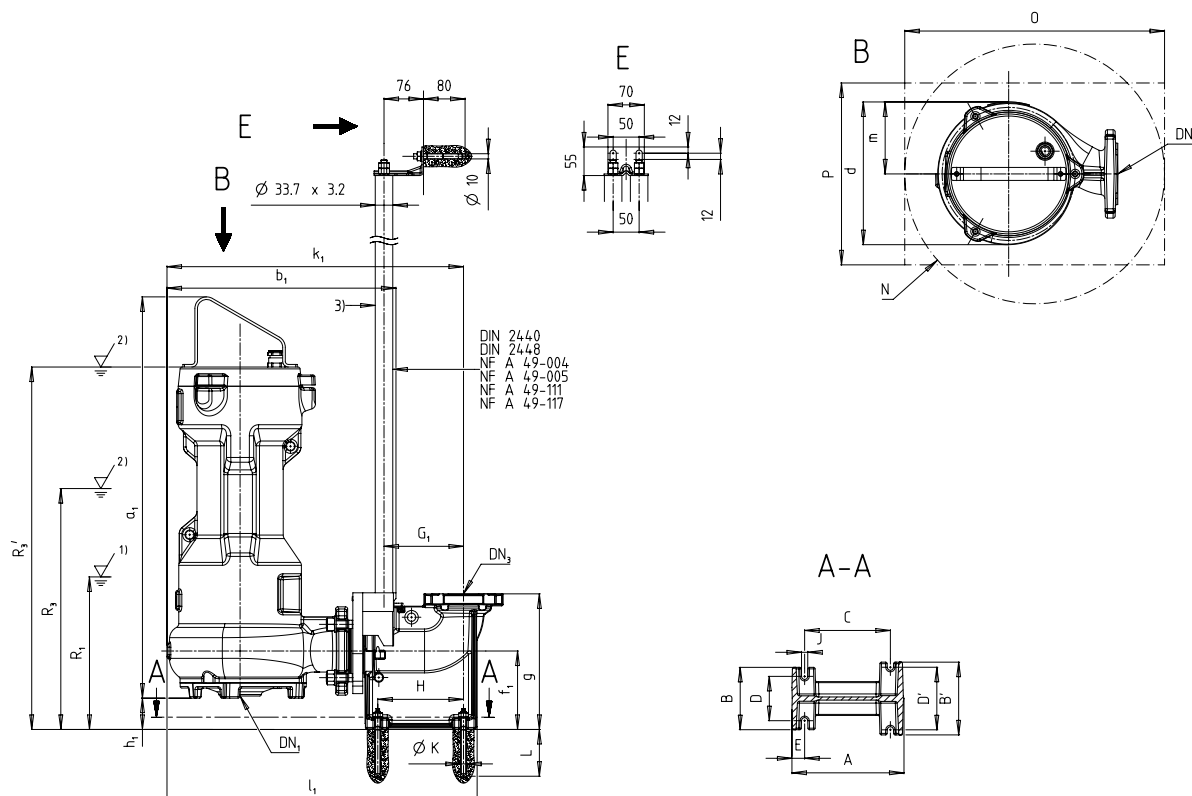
Amarex 65, installazione fissa, installazione fissa, guida per 2 barre
